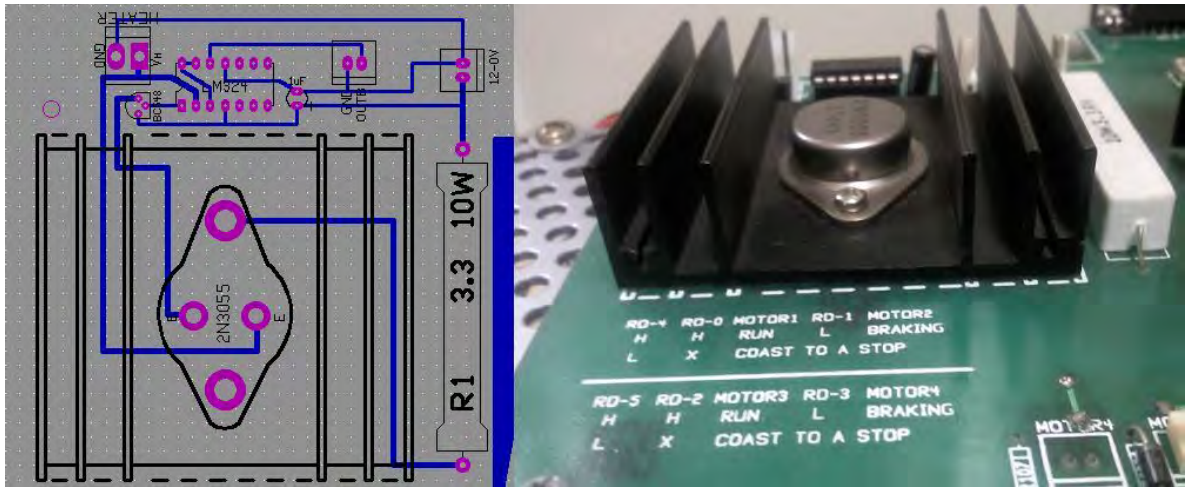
Diseño y fabricación de un circuito que se utiliza como fuente de corriente para el calentamiento de los hornos internos de cada sensor de gas.
